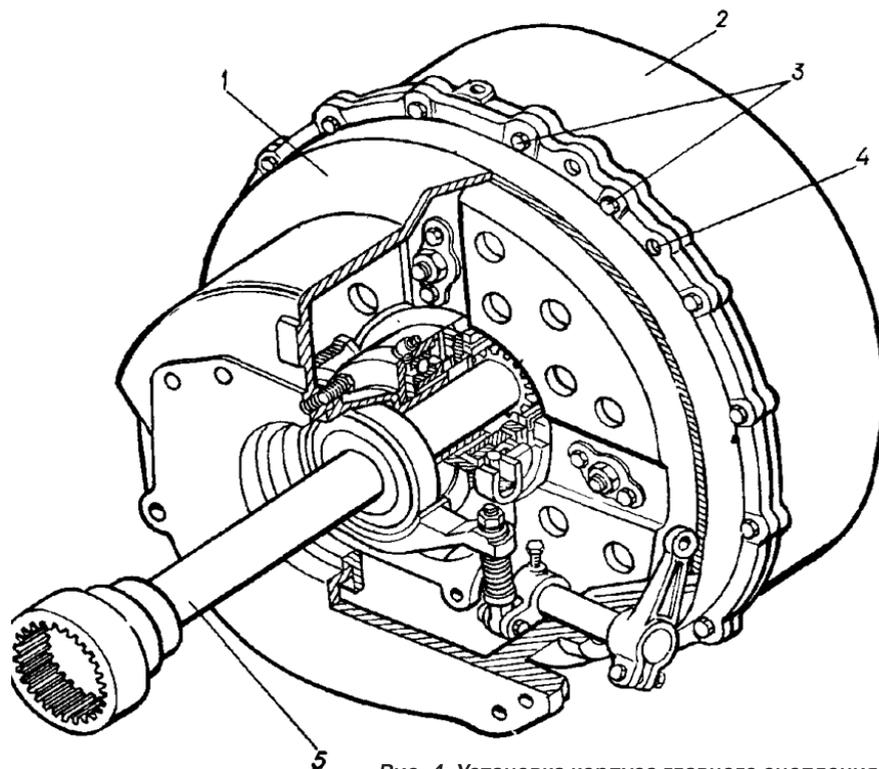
Установка корпуса главного сцепления: 1 — корпус; 2 — картер; 3 — болт; 4 — штифт; 5 — вал
